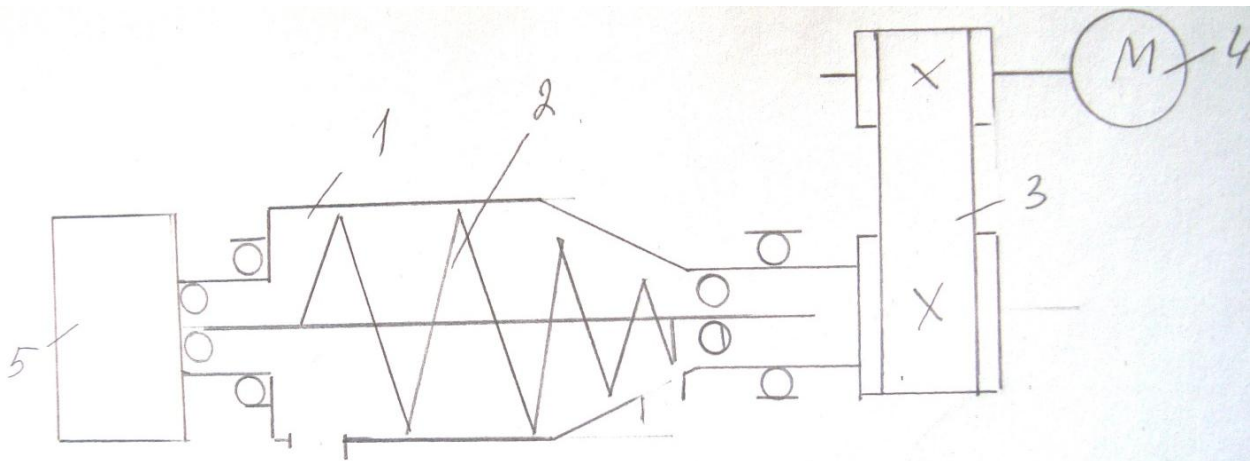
Кінематична схема центрифуги. 1 – ротор; 2 – шнек; 3 – клинопасова передача; 4 – електродвигун; 5 – планетарний редуктор.
